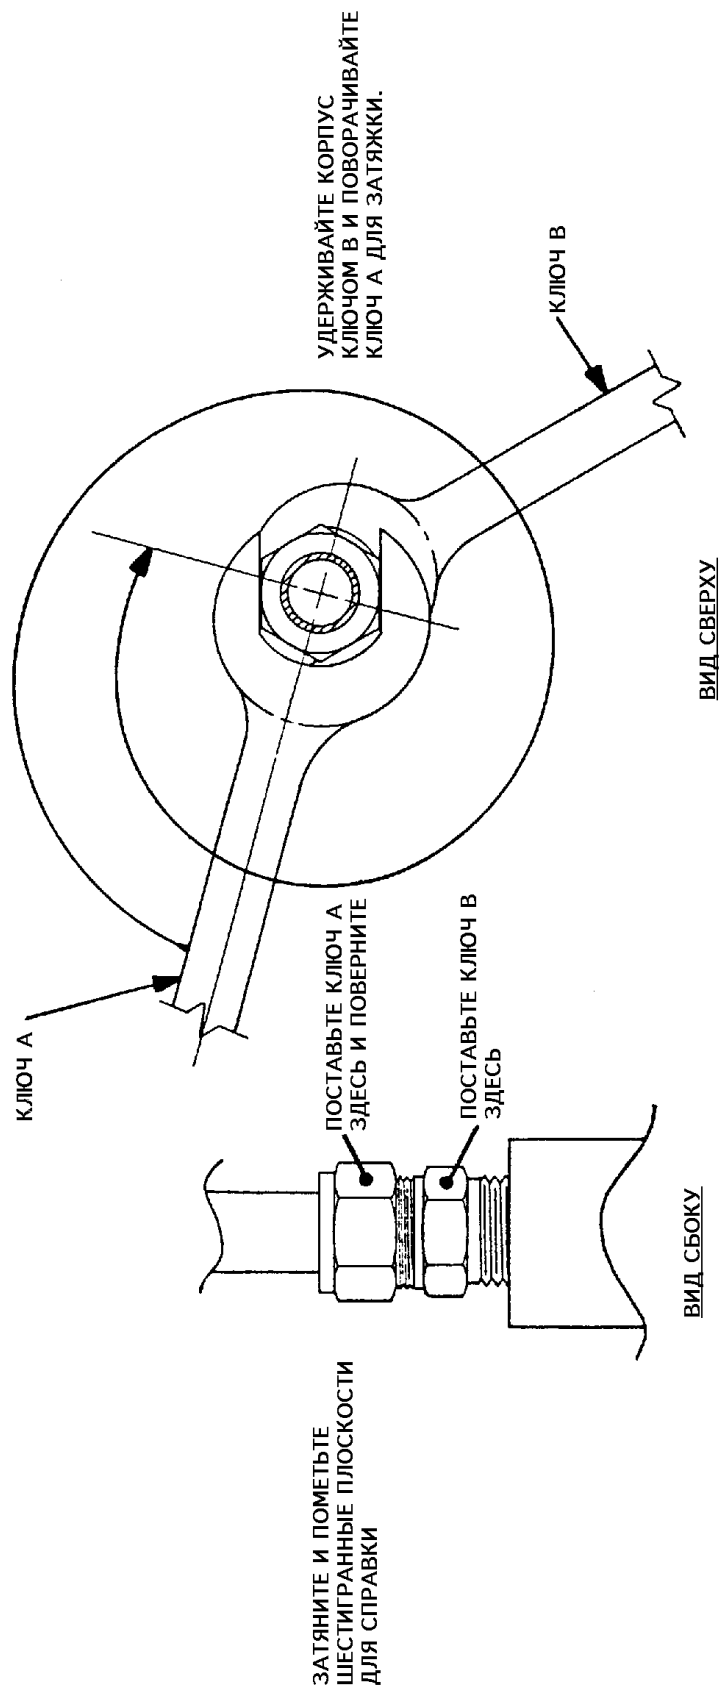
Порядок затяжки соединителя с внешней резьбой
